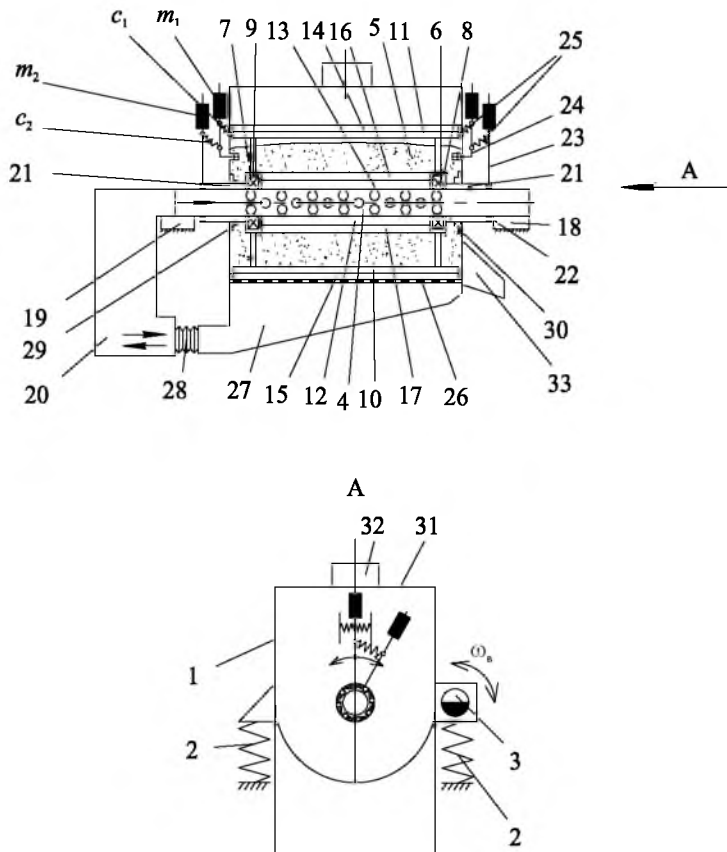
Віброозонуюча сушарка з переміщуючими лопатями і маятниковими механізмами вільного ходу: 1 — камера U-подібної форми; 2 — пружини; 3 — вібробуджувач; 4 — газорозподільна решітка; 5 — зернова сировина; 6, 7 — корпуси підшипників; 8, 9 — підшипники; 10—13 — лопаті-перемішувачі; 14-17 — еластичні скребки; 18, 19 — опори; 20 — система подачі-відбору сушильного агента; 21 — втулка; 22 — маятникові механізми; 23, 24 — маятники; 25 — пружини; 26 — перфороване днище; 27 — дифузор; 28 — еластичне з'єднання; 29, 30 — пружні вставки; 32 — завантажувальний отвір; 33 — розвантажувальний лоток
